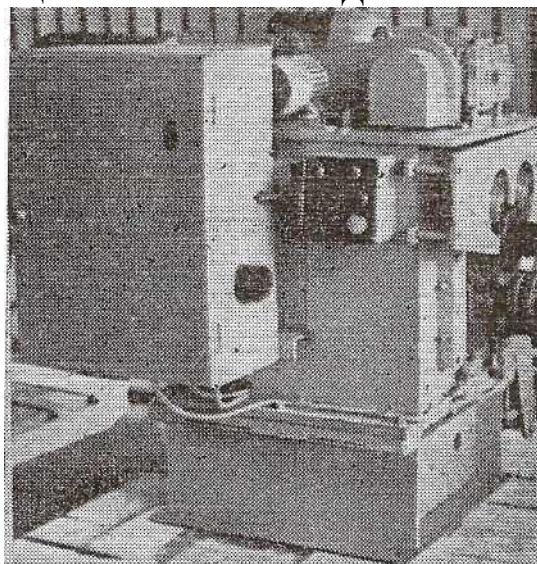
Механизм для отбортовки под бандажное соединение СТД-519
